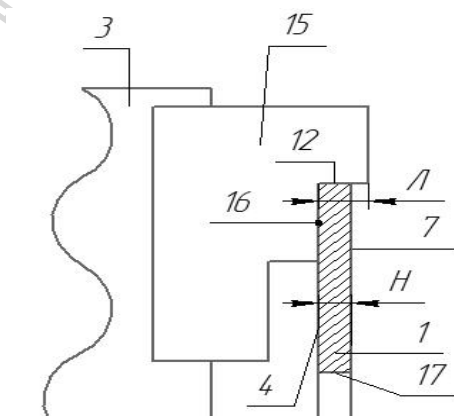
Схема базирования и закрепления за обработанный наружный диаметр детали «Фланец».
